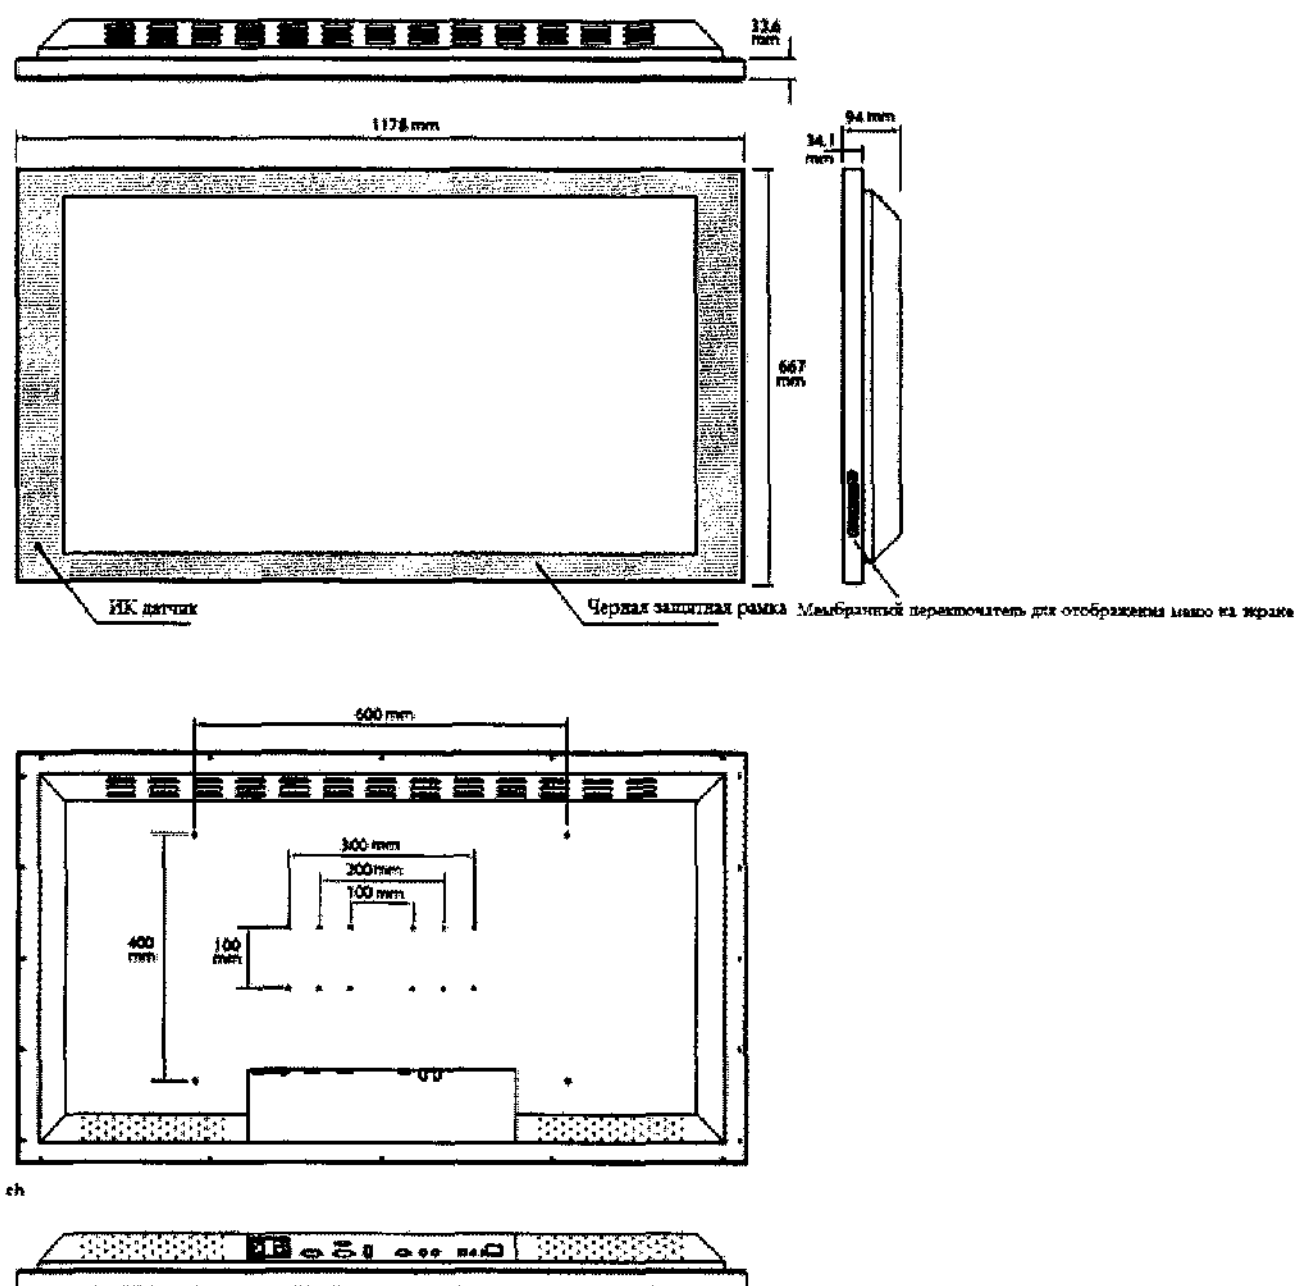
Габаритный чертеж Монитора FS-S4601DT
